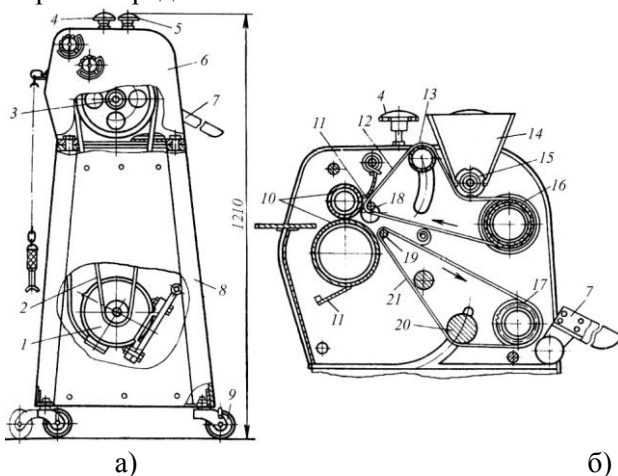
Эскиз закаточной машины: а – общий вид; б – закаточная головка: 1 – электродвигатель; 2 – клиноременная передача; 3 – вал; 4, 5 – винты; 6 – закаточная головка; 7 – лоток; 8 – станина; 9 – каток; 10 – раскатывающий валок; 11 – пластинчатые ножи; 12, – ленточные транспортеры; 13 – натяжной валик; 14 – воронка; 15 – валик мукопосыпателя; 16 – приводной барабан; 17 – приводной барабан; 18, 19 – валики; 20 – натяжной валик
